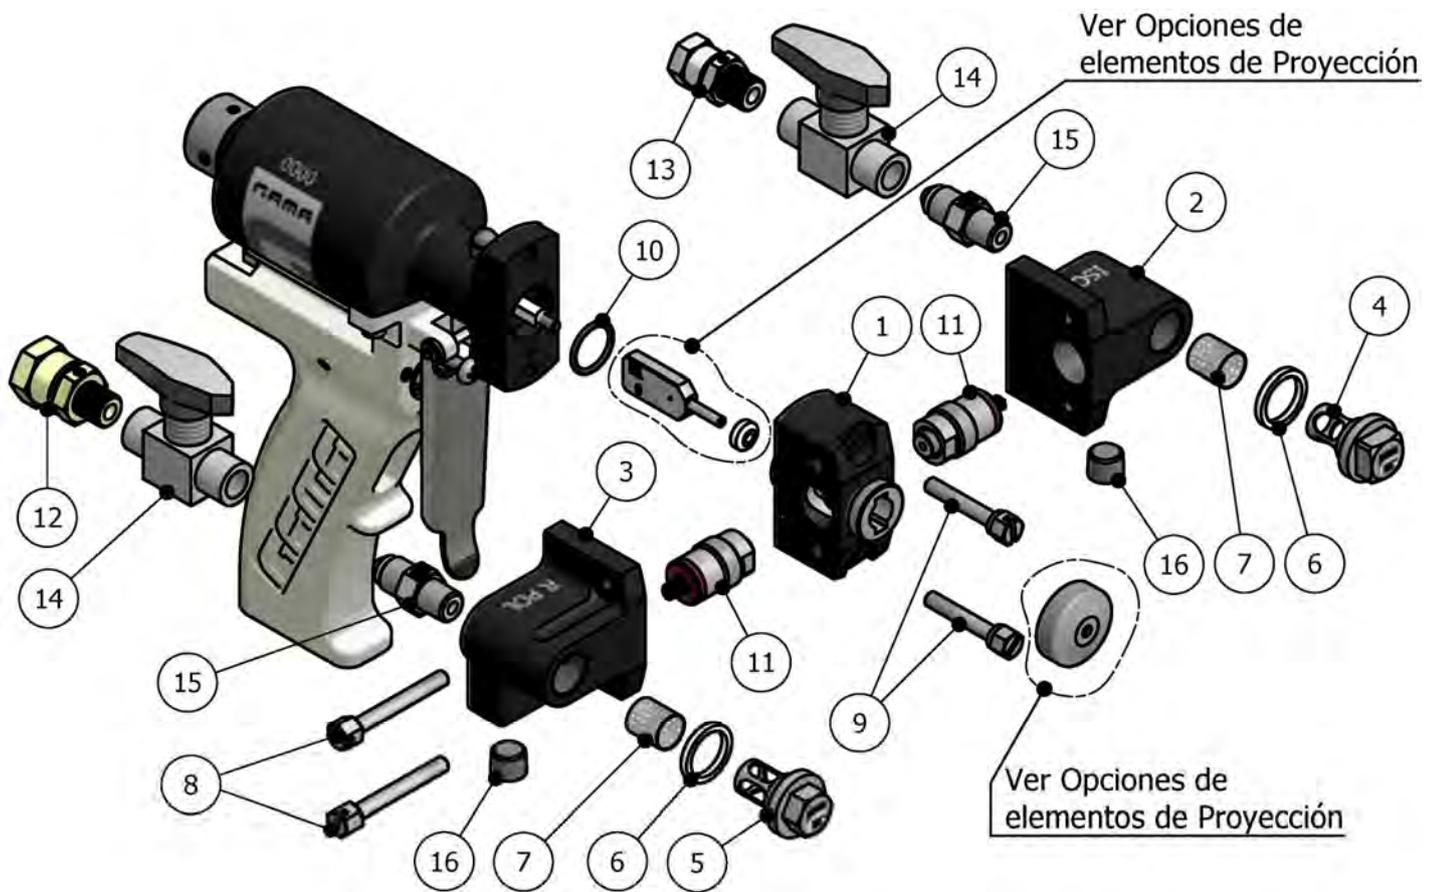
Ensamblaje Final (OPCIONAL), Pistola Master
